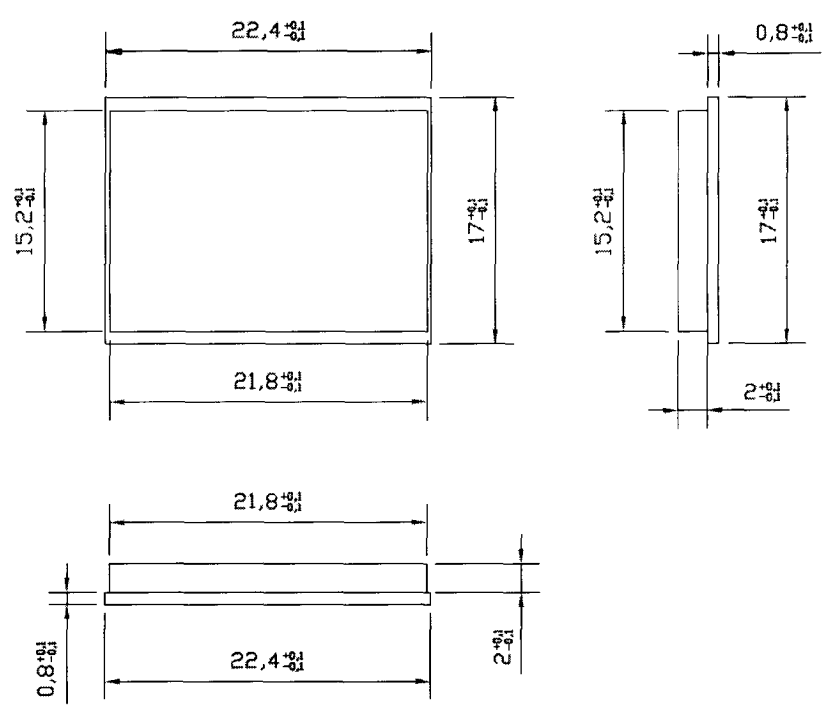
Габаритно-присоединительные размеры модуля MGG2217
